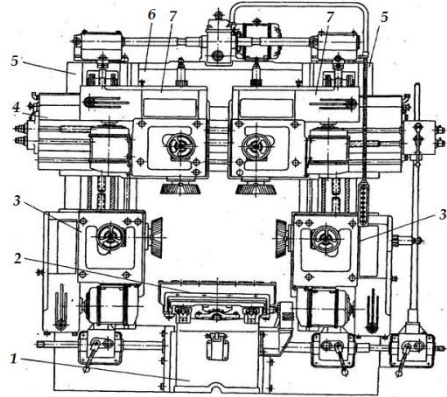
Поздовжньо-фрезерний верстат
